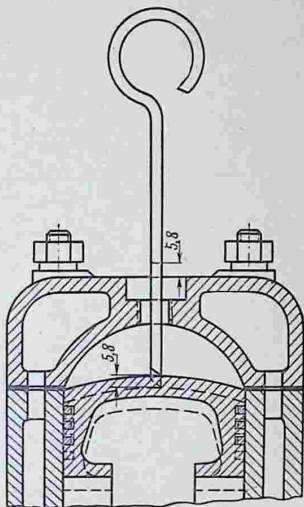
Положение поршня двигателя ПД-10М при регулировке зажигания.
